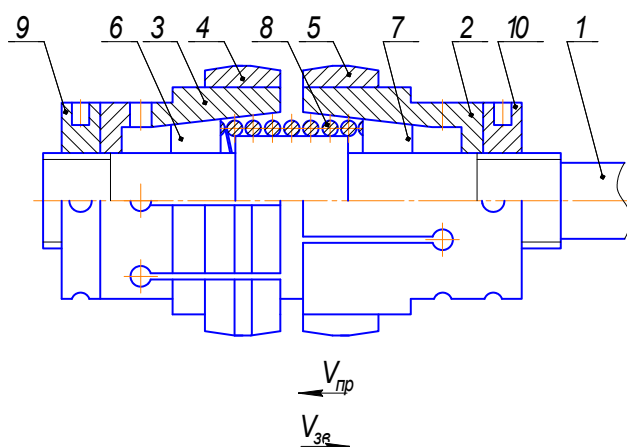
Пристрій для ФАБО внутрішніх циліндричних поверхонь, 1 – оправка; 2, 3 – втулка розрізна; 4, 5 – бруски антифрикційні; 6, 7 – втулки корпусні; 8 – пружина; 9, 10 – гайка
